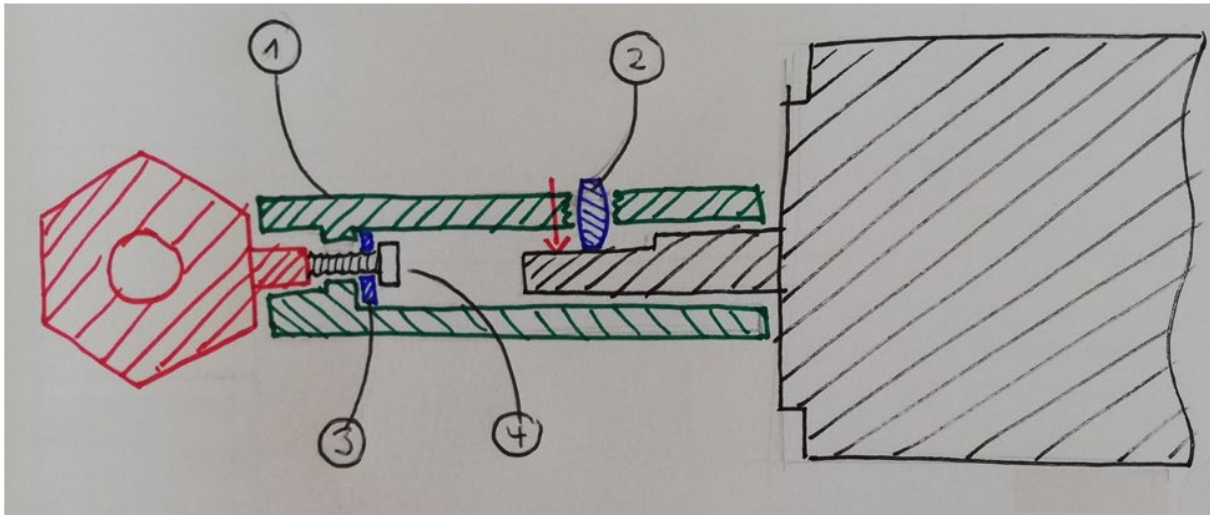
Skizze des Messing-Adapters mit Madenschrauben zur Verbindung von Kugelventil und Stellmotor
